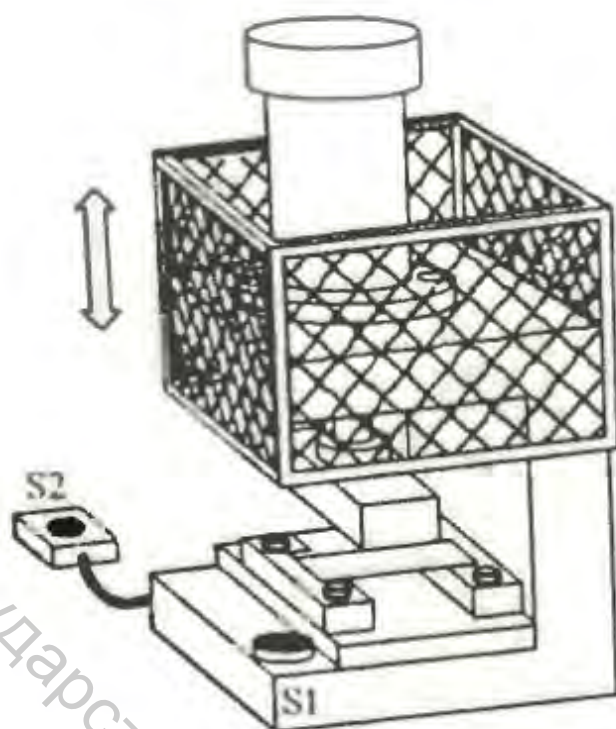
Эскиз устройства штамповки дебелей
